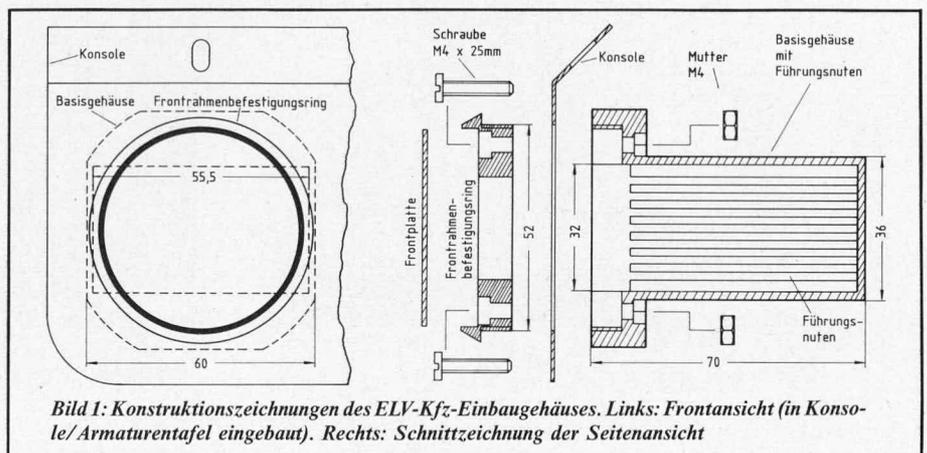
Konstruktionszeichnungen des ELV-Kfz-Einbaugehäuses. Links: Frontansicht (in Konsole/Armaturentafel eingebaut). Rechts: Schnittzeichnung der Seitenansicht
